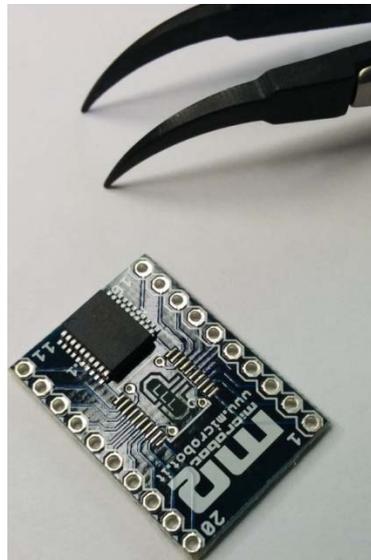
Componente antes de ser soldado en el adaptador
